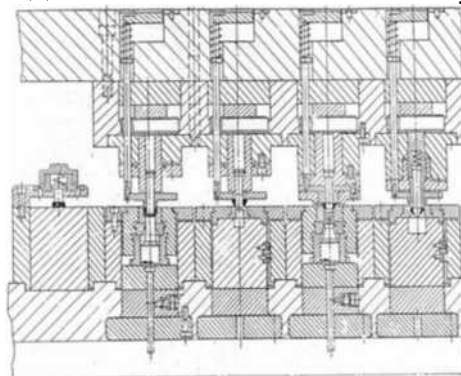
Пример конструкции многопозиционного штампа с линейным расположением инструмента для штамповки деталей типа тарелки
